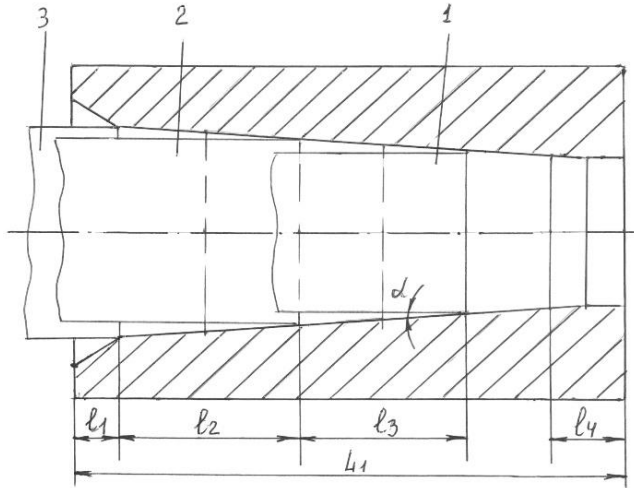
Схема до розрахунку параметрів робочої поверхні матриці для центрування заготовок трьох типорозмірів: 1 – для $\varnothing 130$ мм; 2 – для $\varnothing 150$ мм; 3 – для $\varnothing 170$ мм
